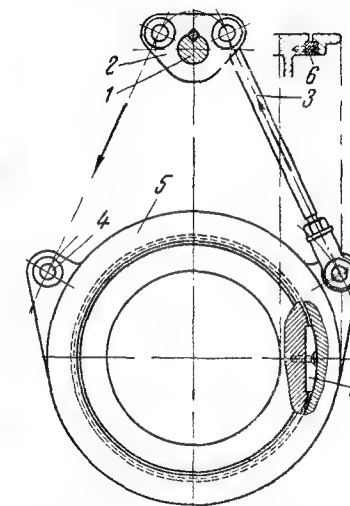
Привод регулирующего кольца (на сухарях) двумя тягами от регулирующего вала.
